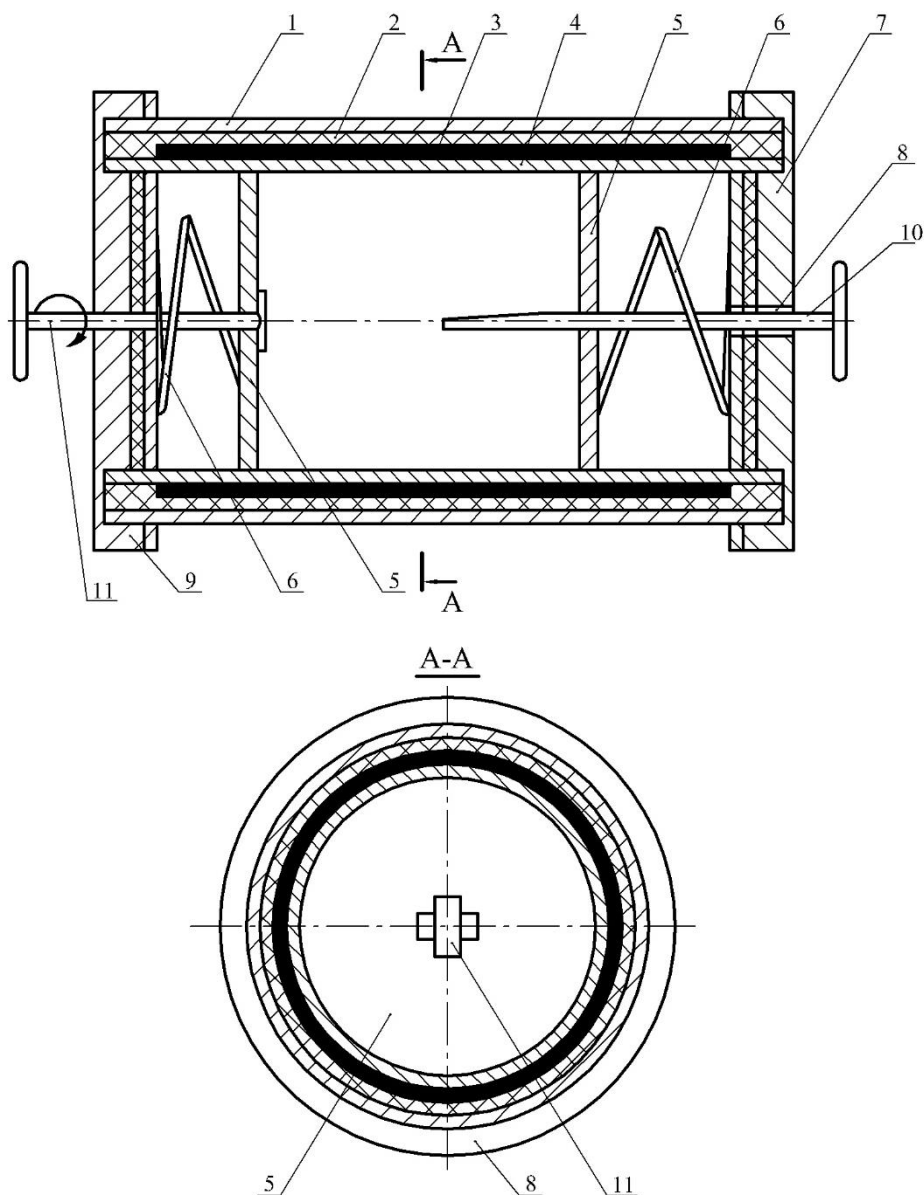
Пристрій для теплової обробки формованих кулінарних виробів без оболонки: 1 – зовнішній пластиковий корпус; 2 – шар ізоляційної плівки; 3 – плівковий електронагрівач; 4 – внутрішній пластиковий корпус; 5 – пластикові опорні пластини; 6 – металеві пружини; 7, 9 – кришки з круглим та прямокутним отворами, відповідно; 8 – круглий отвір для термометра; 10 – термометр; 11 – обертовий фіксатор пружини
